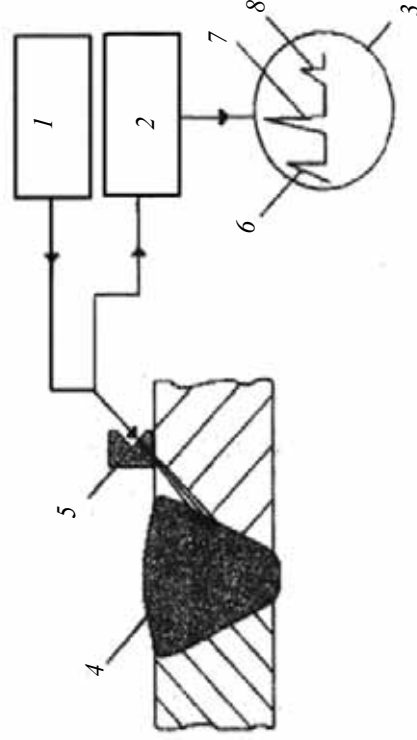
Ультразвуковой контроль сварных соединений:
